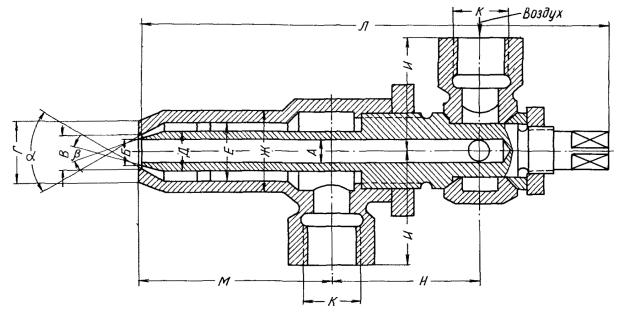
Форсунка высокого давления конструкции Шухова [6]
